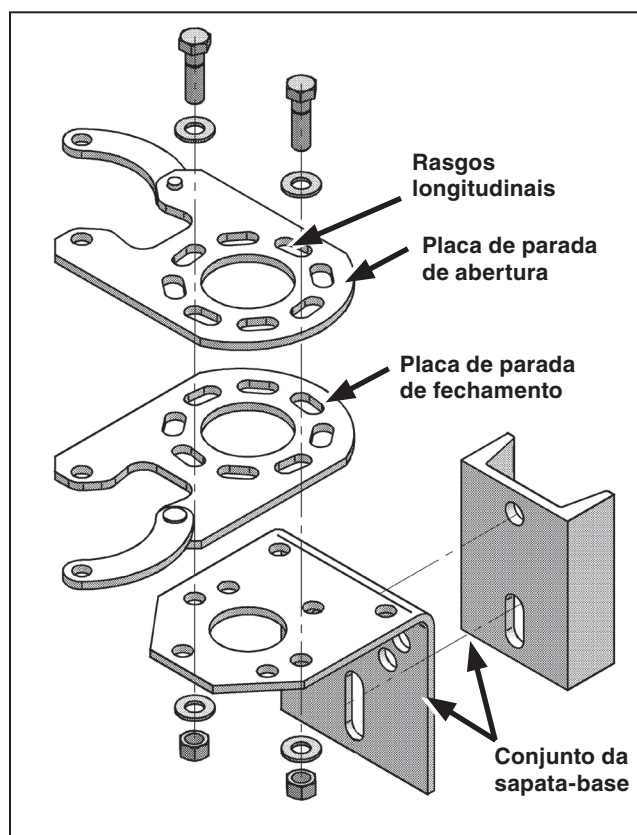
Placas de parada e conjunto da sapata-base—vista explodida.
